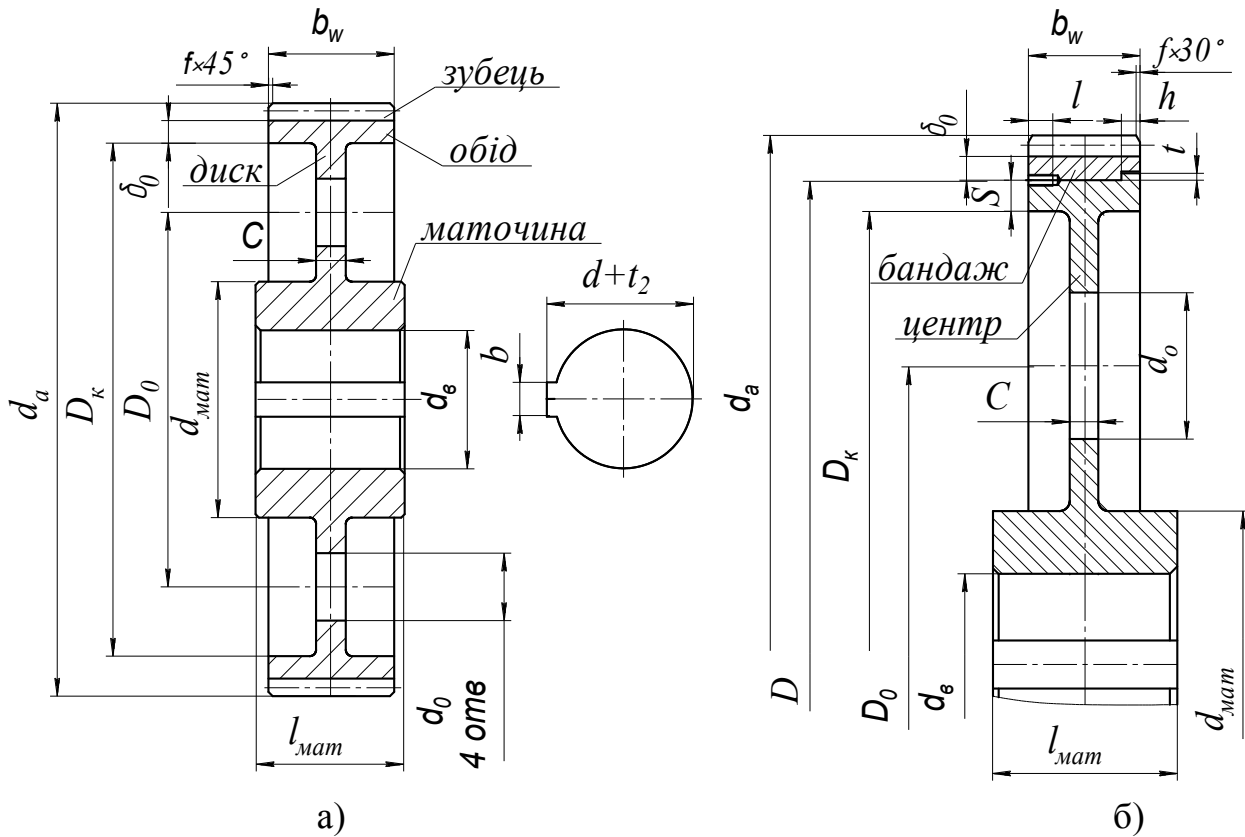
Конструкції циліндричних зубчастих коліс: а) колесо, яке виготовлено штампуванням; б) збірне зубчасте колесо
